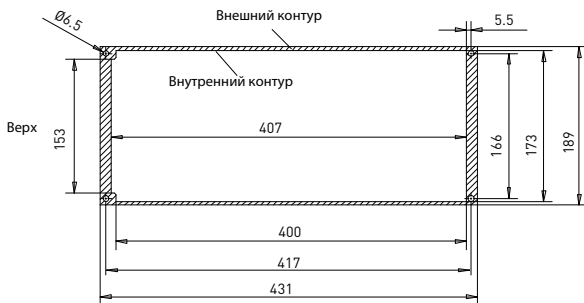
Размеры выреза для фланцевого крепления приводов типоразмеров M15 (единица: мм)
